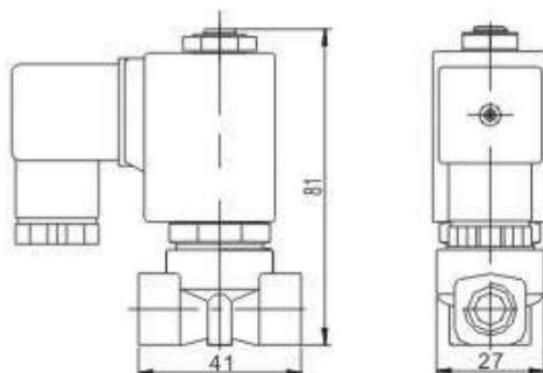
Габаритные и присоединительные размеры клапана типа EV210WR
